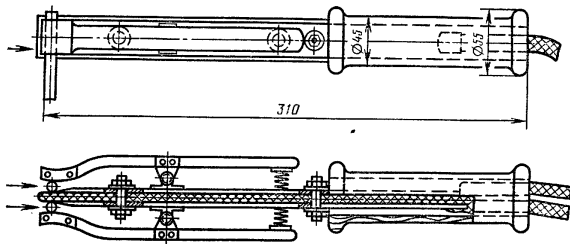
Электрододержатель для трехфазной сварки двумя параллельными электродами
